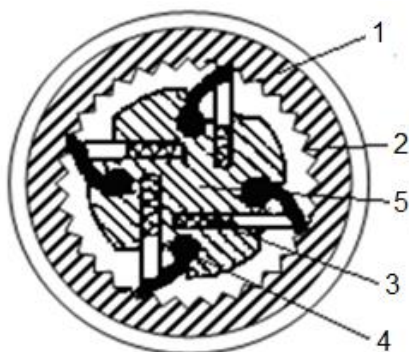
Поворотный механизм с четырьмя собачками
